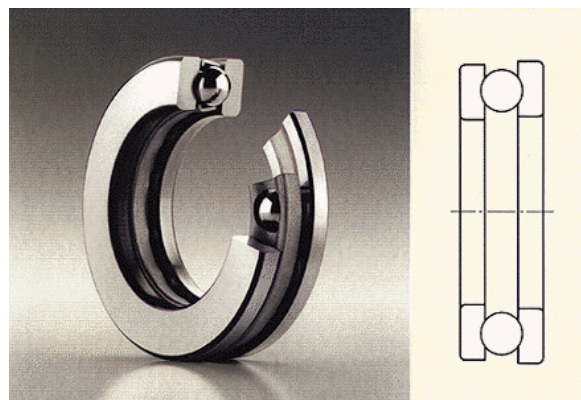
Rodamiento axial de bolas de simple efecto.
